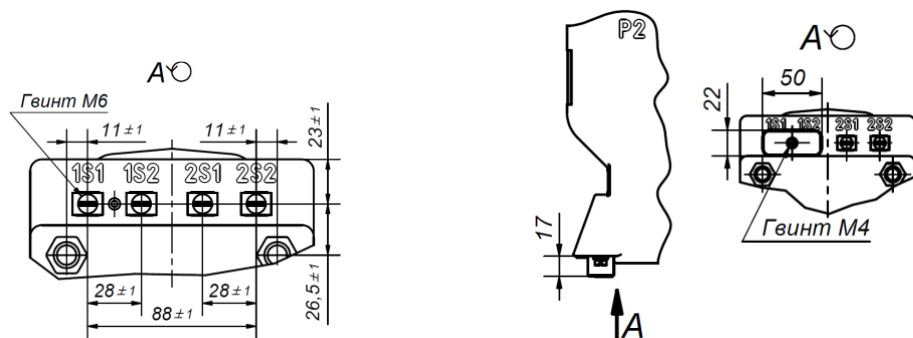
Чертеж выводов вторичных обмоток трансформаторов TCS2-12-11..... расположенных на нижней опорной поверхности корпуса (код конструкции "4")
